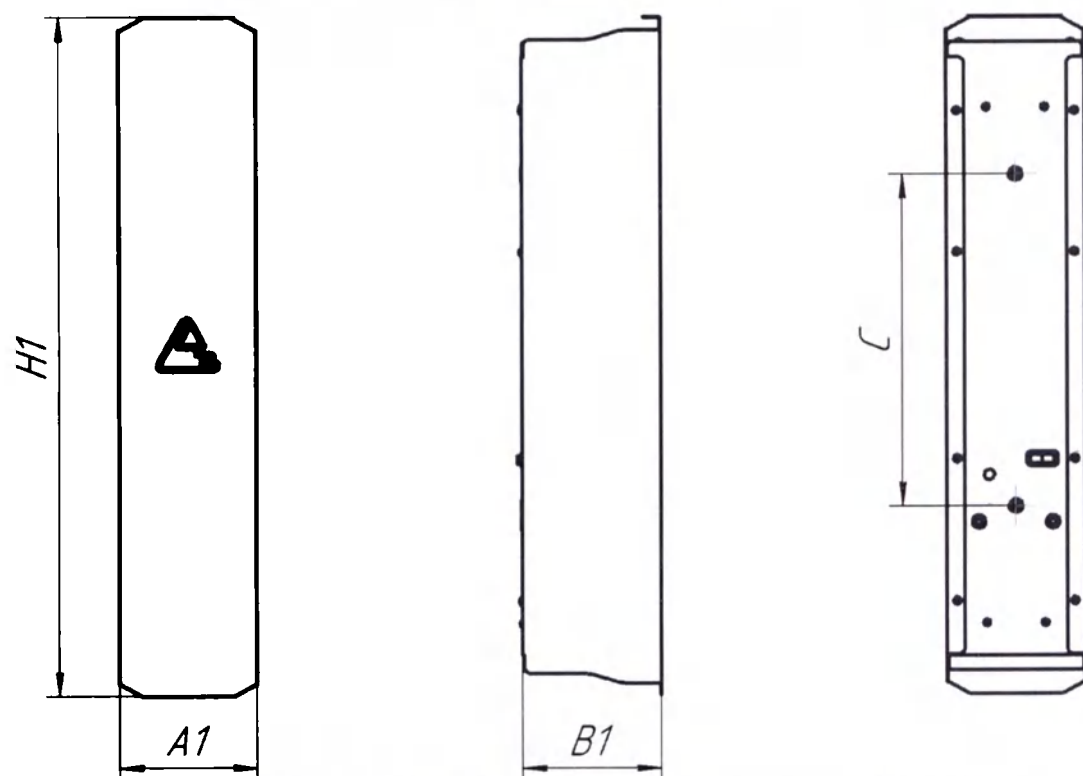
габаритные размеры рециркулятора без опоры.
